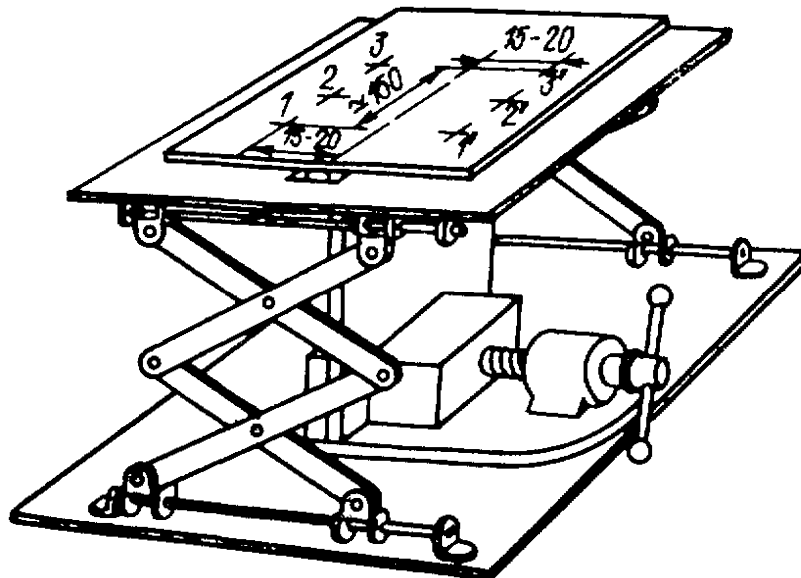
Розмітка проби перед зварюванням для визначення вкорочення
